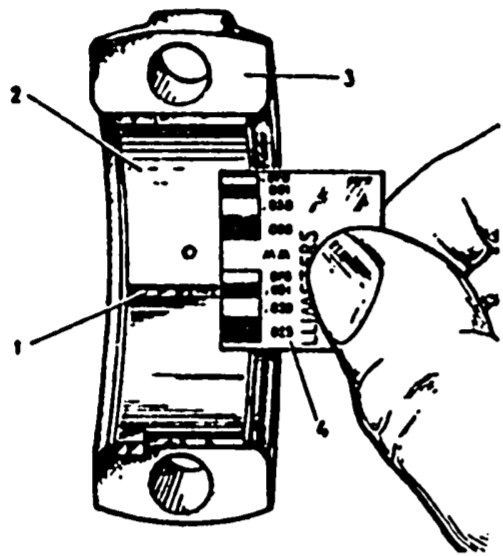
Измерение с помощью шкалы ширины калиброванной проволоки после сплющивания: 1 - калиброванная проволока; 2 - вкладыш; 3 - крышка шатунного подшипника; 4 - шкала для калиброванной проволоки
